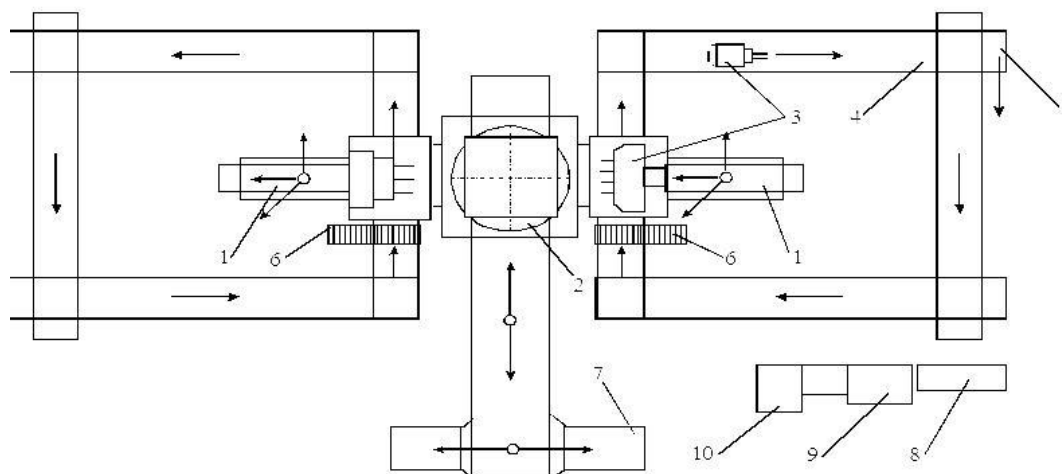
Схема переналагоджуваного агрегатного верстата:
